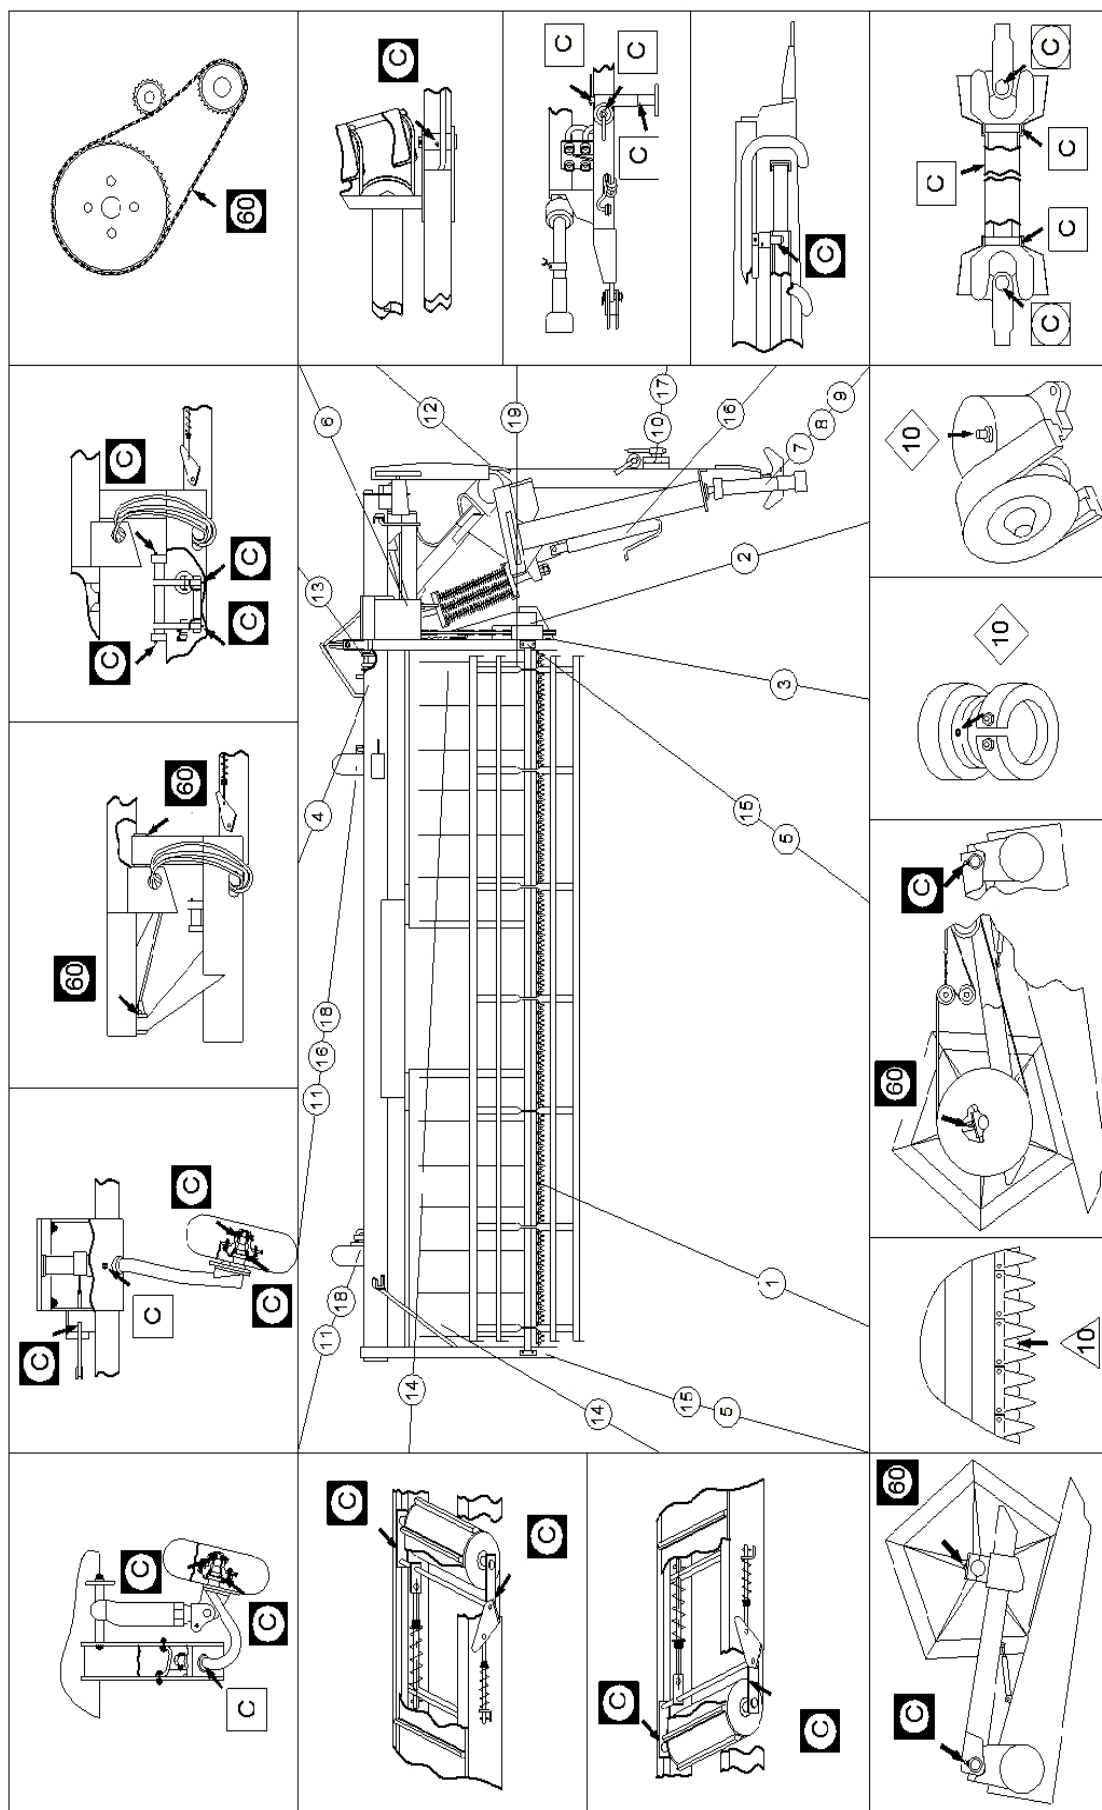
Схема смазки жатки валковой зерновой ЖВЗ-7,0П
